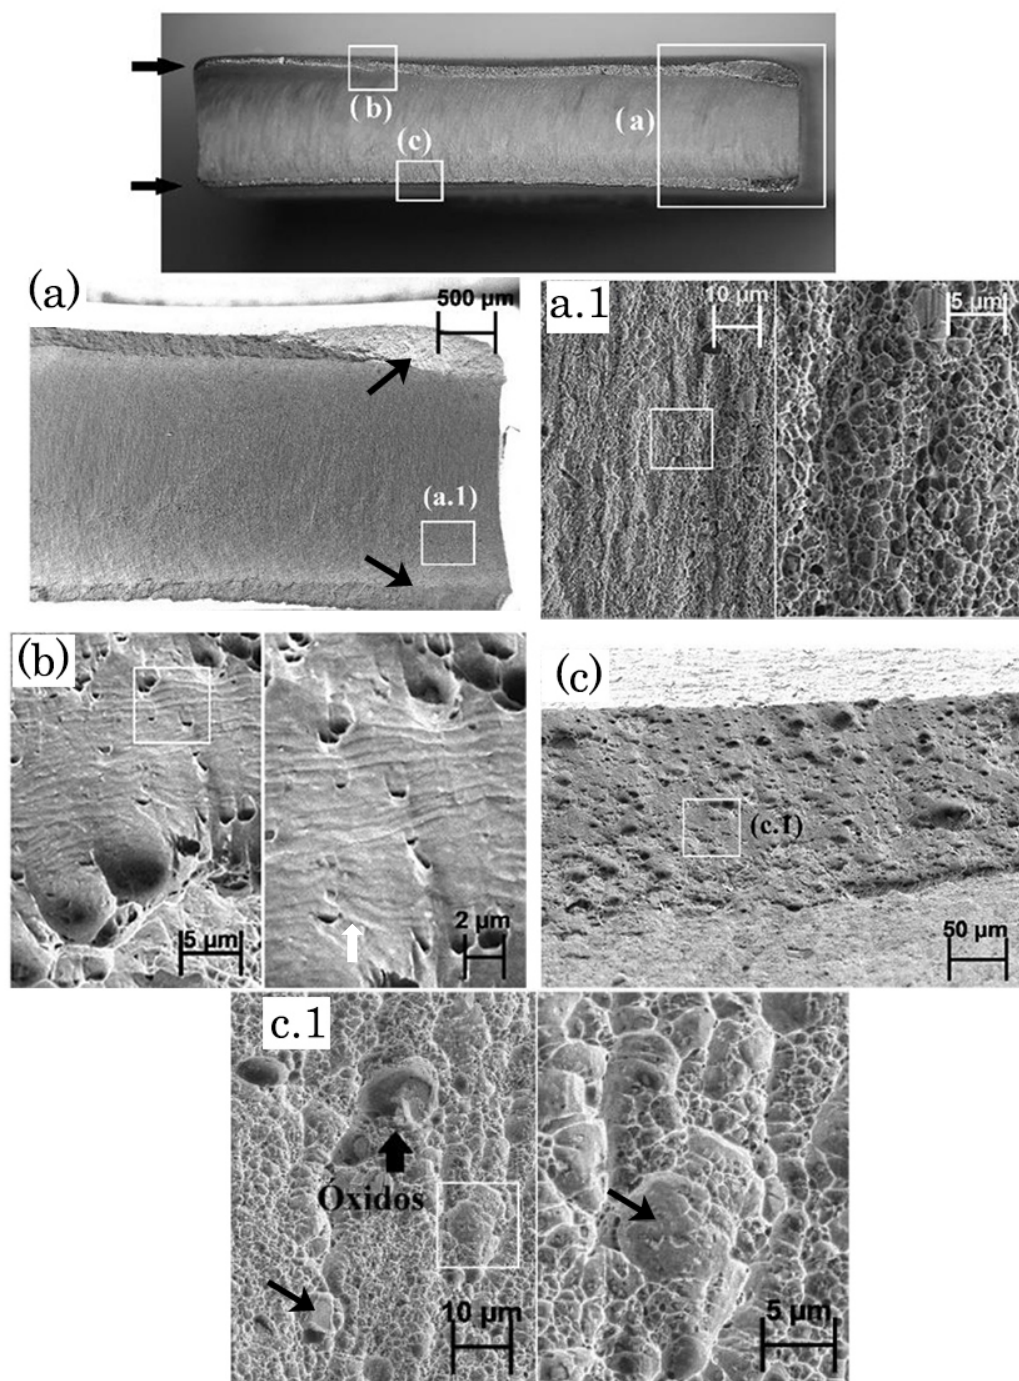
Superfície de fratura de amostra da soldadura DBPR-65-663_P1.
